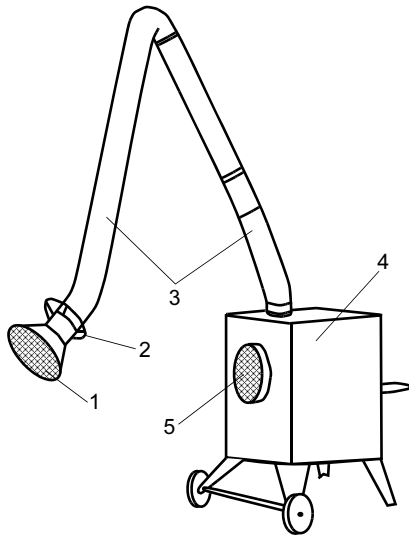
Передвижная малогабаритная фильтровентиляционная установка: 1 — вытягивающая воронка; 2 — кольцо захвата; 3 — гибкий рукавный воздухопровод; 4 — фильтровентиляционный агрегат с малогабаритными фильтрами; 5 — выход очищенного воздуха
